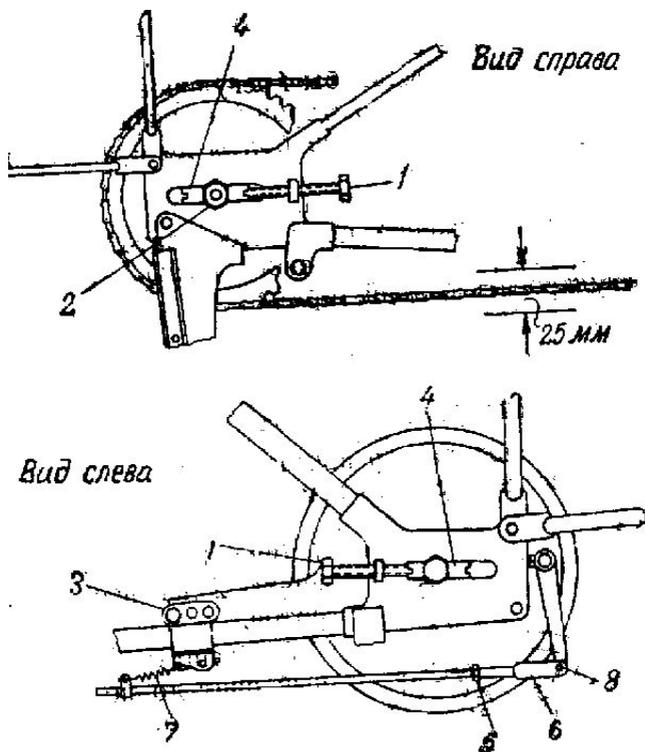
Натяжение задней цепи и регулировка тормозов:
